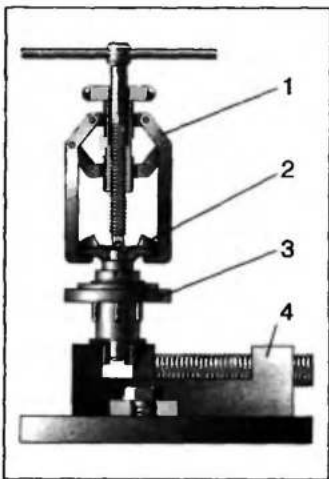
Снятие крыльчатки насоса с помощью съемника: 1 — съемник; 2 — крыльчатка; 3 — корпус насоса; 4 — тиски
